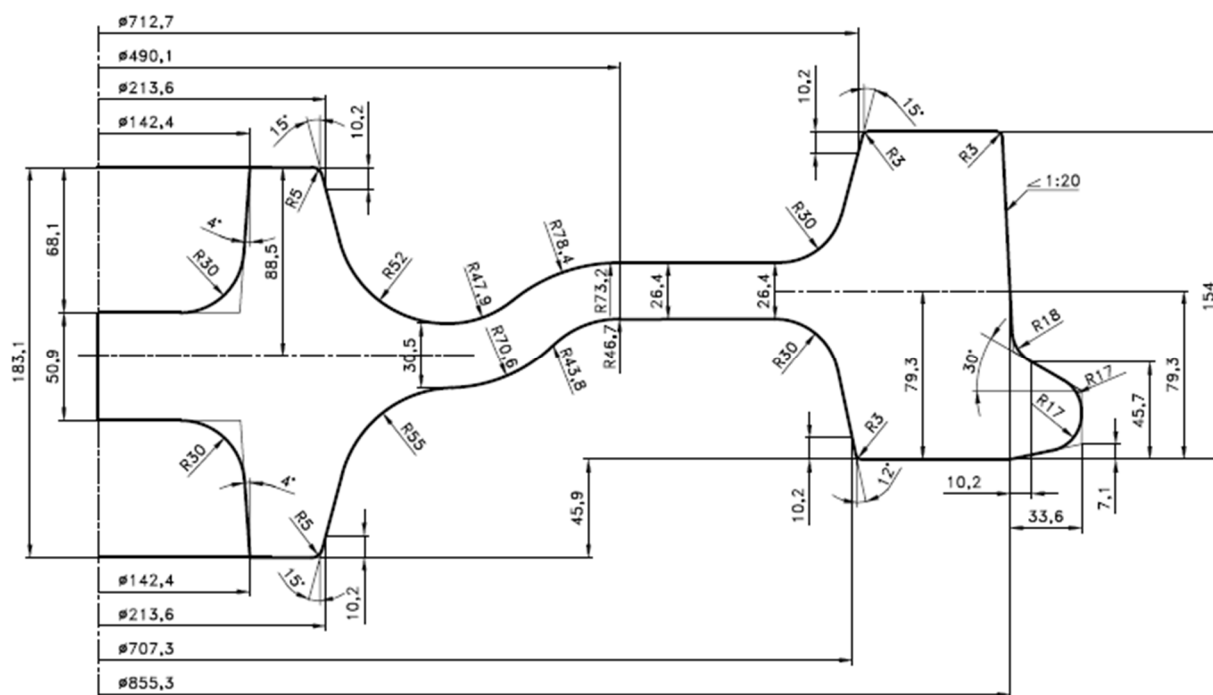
Контур сечения чернового колеса диаметром 855 мм, прокатанного на колесопрокатном стане (калибровка для КПС)
